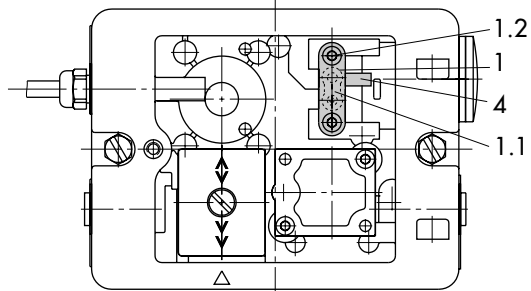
· Montaggio diretto con posizionatore tipo 3766
